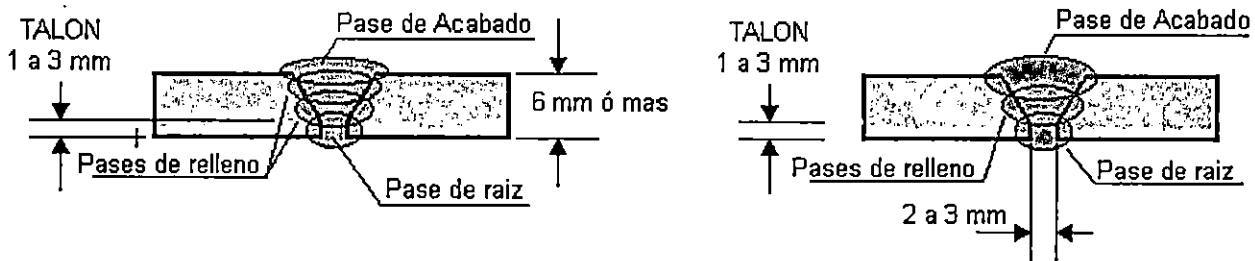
Ejemplos de Secuencias de Pases de Soldadura en uniones a tope con bordes en V.
